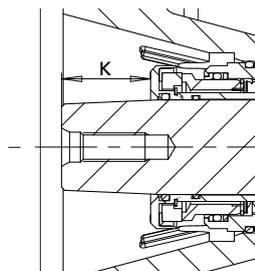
Контрольный размер «К» от конца вала до сдвоенного картриджного торцового уплотнения KSB
